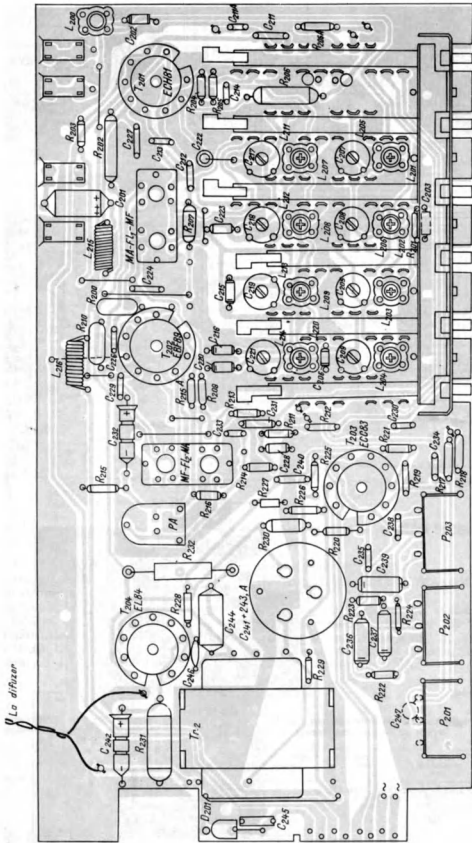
Ansamblul placă cabaj imprimat
